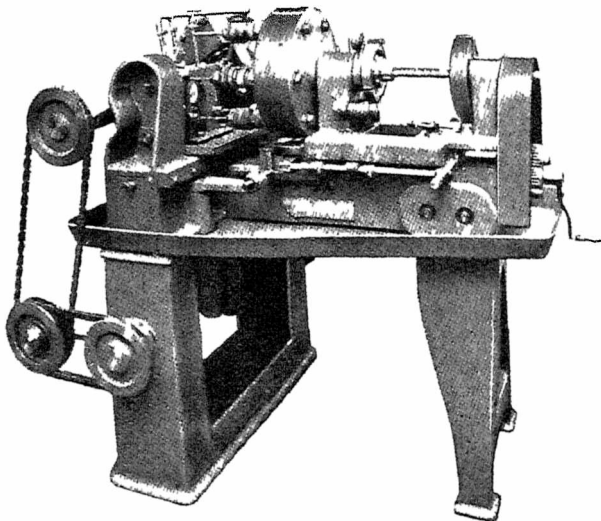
Szlifierka f-my The Churchill Machine Tool Co. Ltd. do obróbki hartowanych wielołożbkowych wałków.
